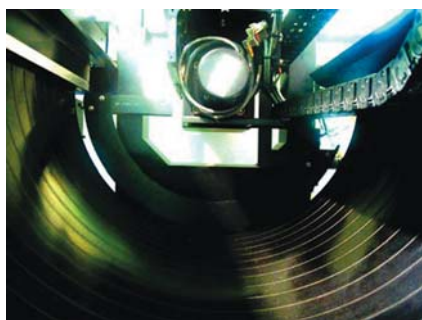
Внутренний барабан фотоплоттера EQUINOX
